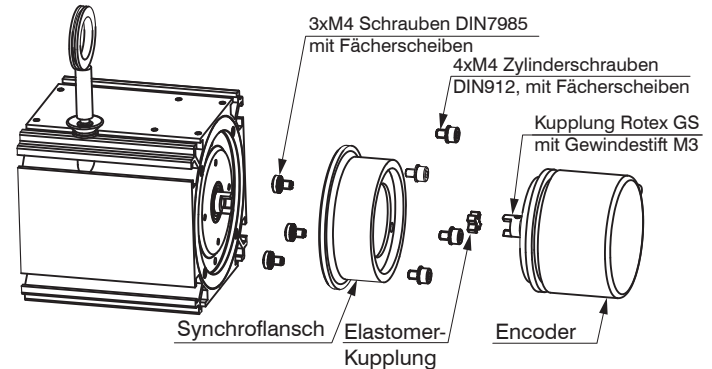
Montage von Flansch und Encoder, WDS-Pxxx
